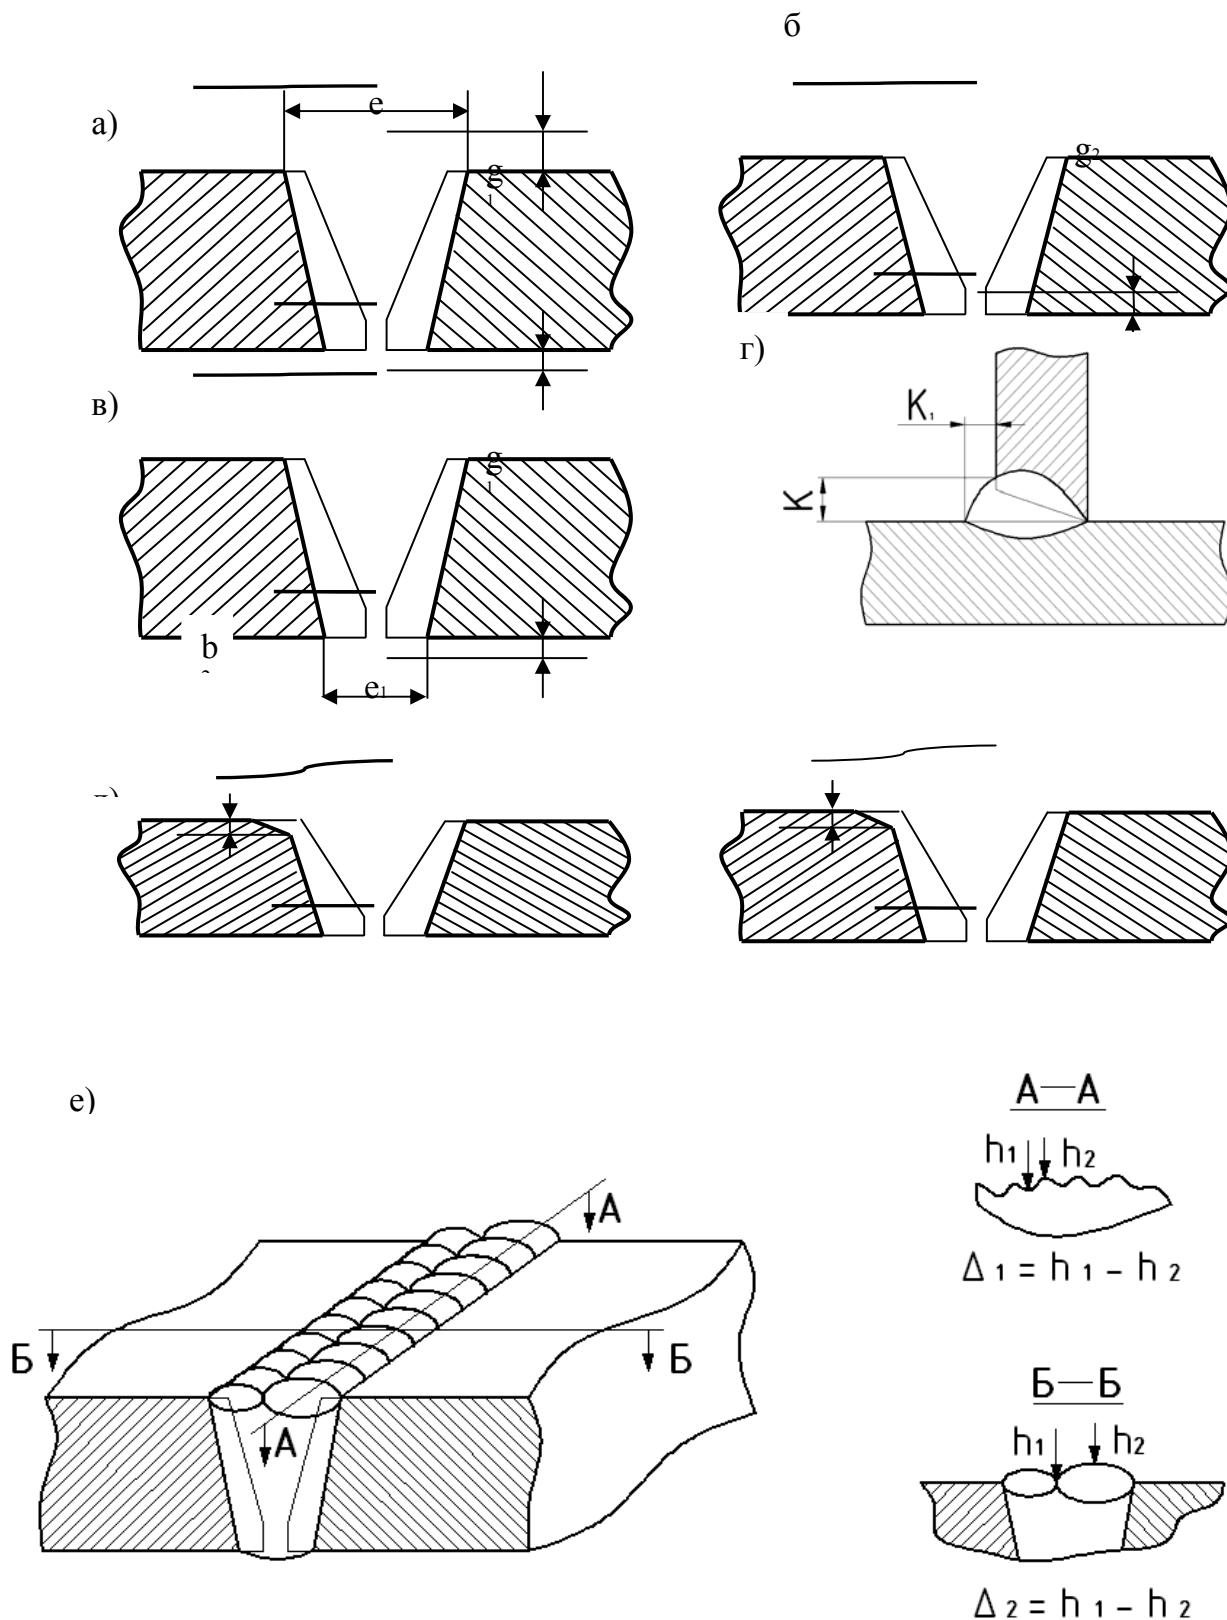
Схема замеров сварного шва и его дефектов
